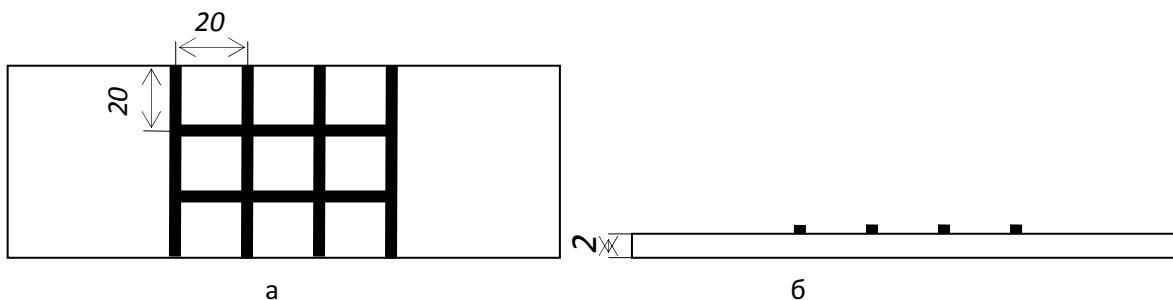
Образец с искусственным «жестким» каркасом в виде наплавки: а – вид сверху; б – вид сбоку
